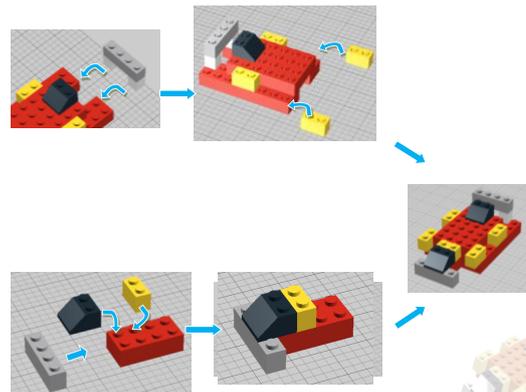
PLANO DE MONTAJE – CENTRO DE TRABAJO 2 CELDAS.
